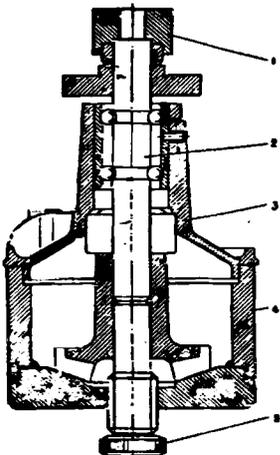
Напрессовка крыльчатки на валик насоса приспособлением А.60430: 1 - опора; 2 - валик насоса; 3 - крышка корпуса насоса; 4 - стакан; 5 - установочный винт
